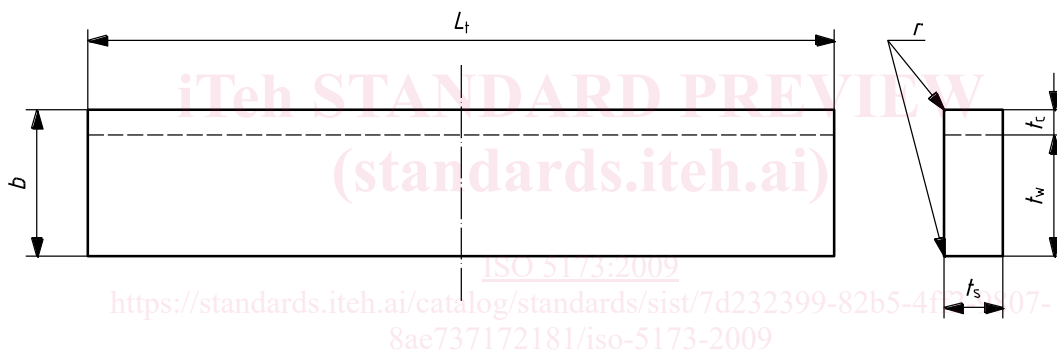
Образец для испытаний на загиб с растяжением боковой стороны для плакировки без стыкового сварного шва (SBC)
